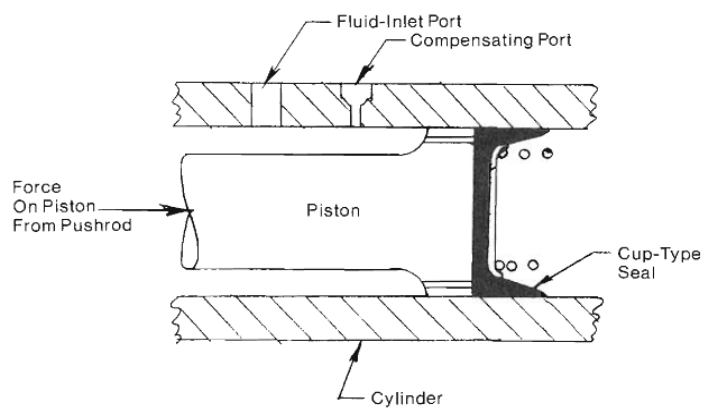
Avanço do pistão com o vedante a estancar a passagem de fluido [2]
